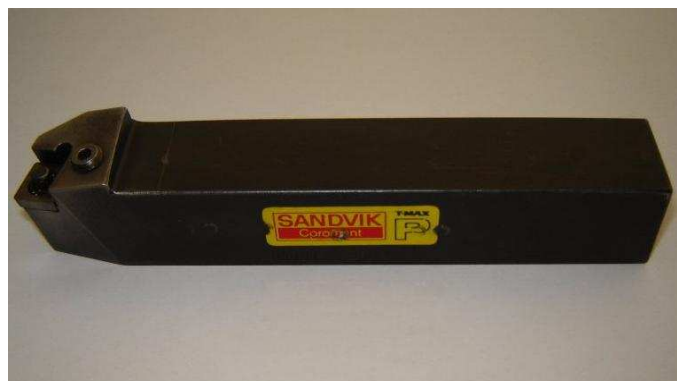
Photo de la plaquette de coupe utilisée.
